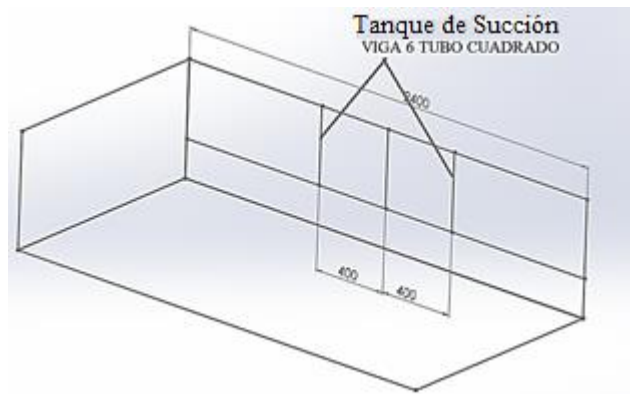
Viga 6 Tubo cuadrado 20 * 2
